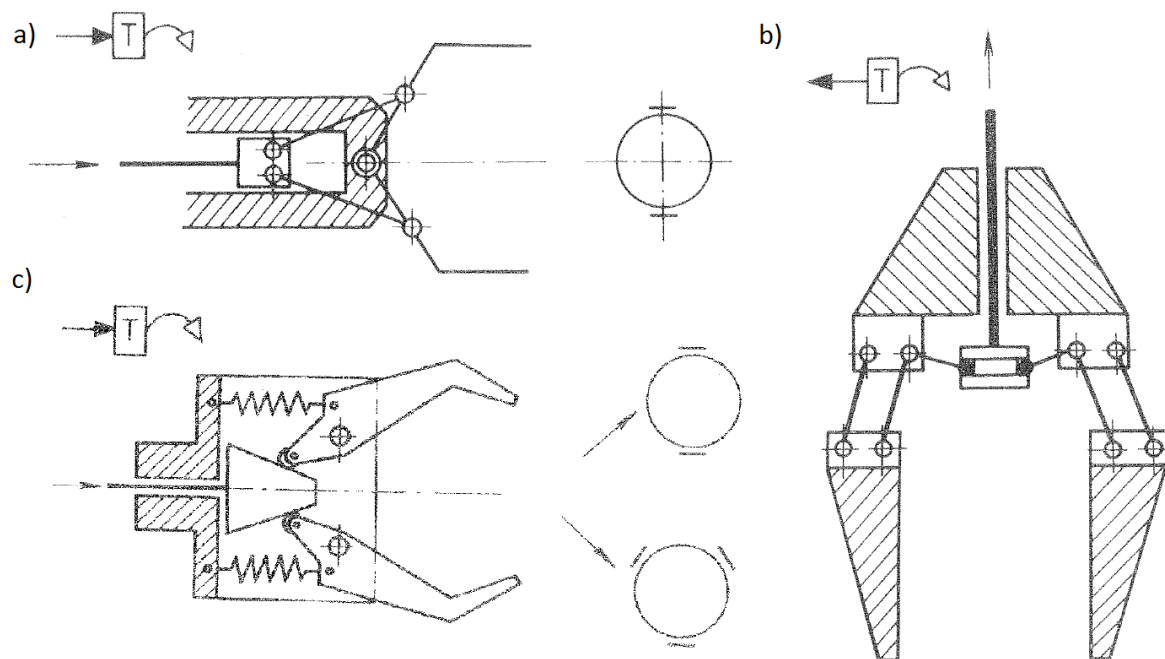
Kinematické uspořádání úchopných hlavíc s jedním aktivním a jedním pasivním prvkem [34]
